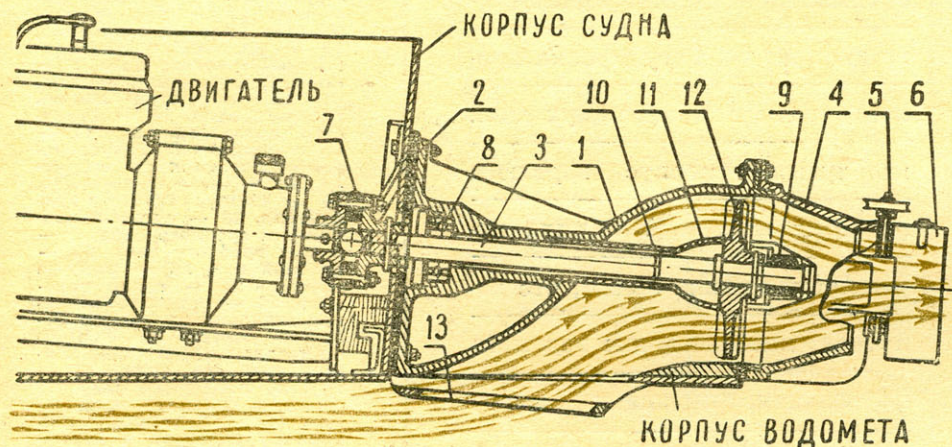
Продольный разрез навесного водометного движителя: 1 — водовод, 2 — фланец, 3 — гребной вал, 4 — сопло, 5 — подвеска рулевого устройства, 6 — рулевые пластины, 7 — соединительная эластичная муфта, 8 — шариковый подшипник гребного вала, 9 — резино-металлический подшипник гребного вала, 10 — защитный кожух вала, 11 — обтекатель вала, 12 — рабочее колесо, 13 — входное отверстие водозаборника.
